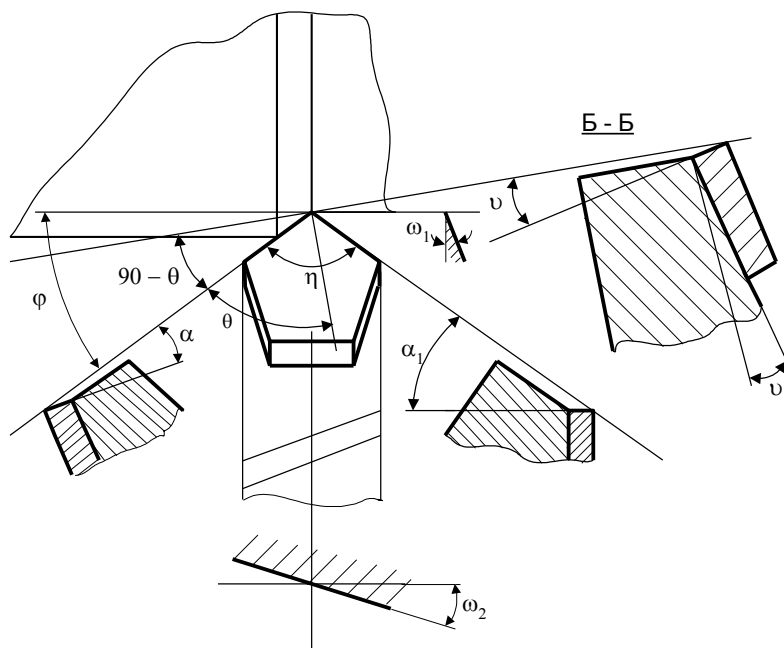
Схема расположения опорной поверхности пластины на державке резца
